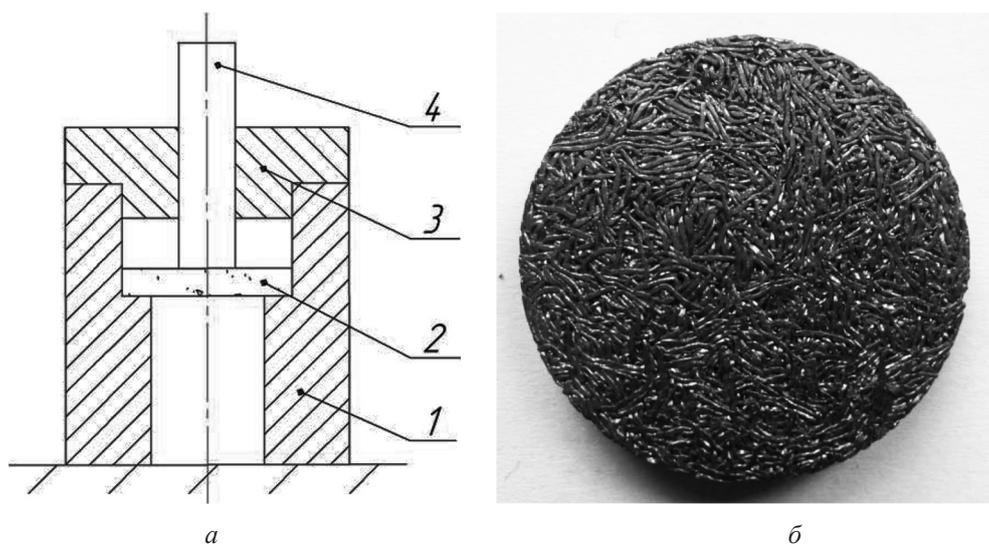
Устройство для оценки качества спекания пористых волокновых материалов (а) и внешний вид образца для проведения испытаний (б)
